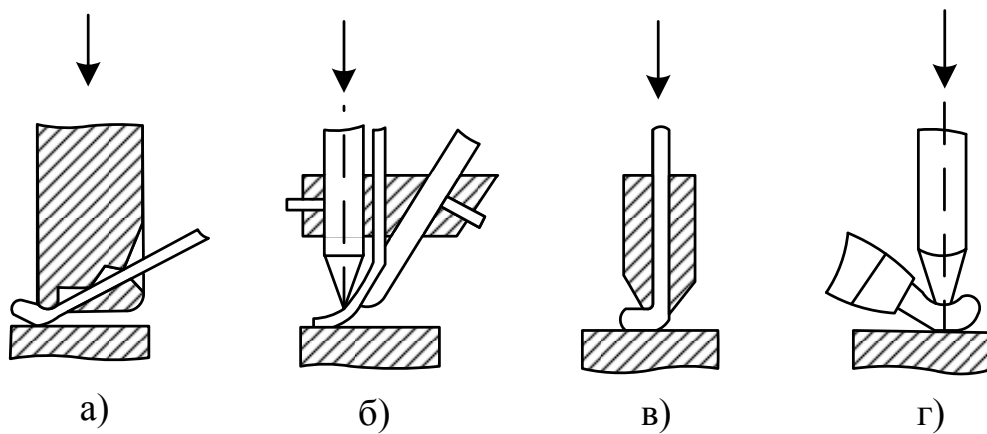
Типи інструментів для проведення термокомпресійного зварювання: а – «платиновий дзьоб»; б – «клин»; в – «капіляр»; г – «голка»
